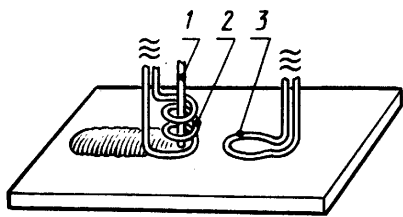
Схема наплавки с расплавлением присадочного металла индукционным способом
